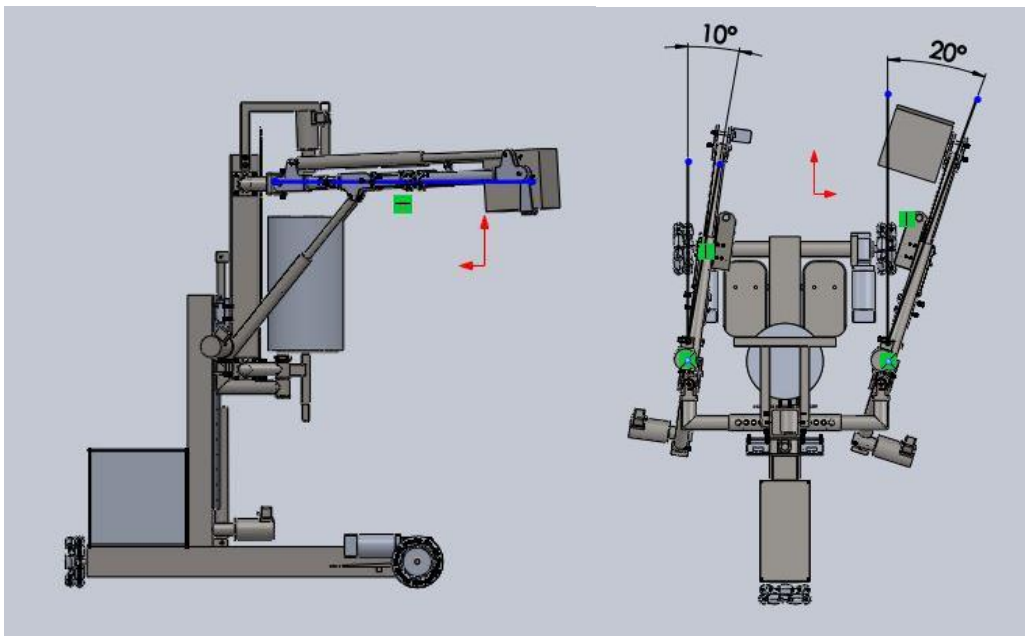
Vistas de la estructura situada en la posición más desfavorable. Fuente propia.
